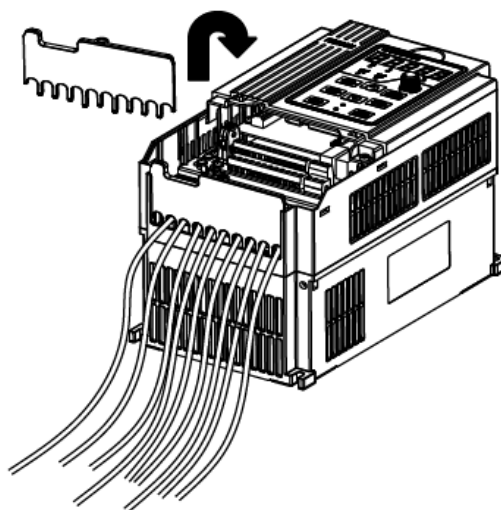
(g). Демонтаж и монтаж пластины разделения проводов
